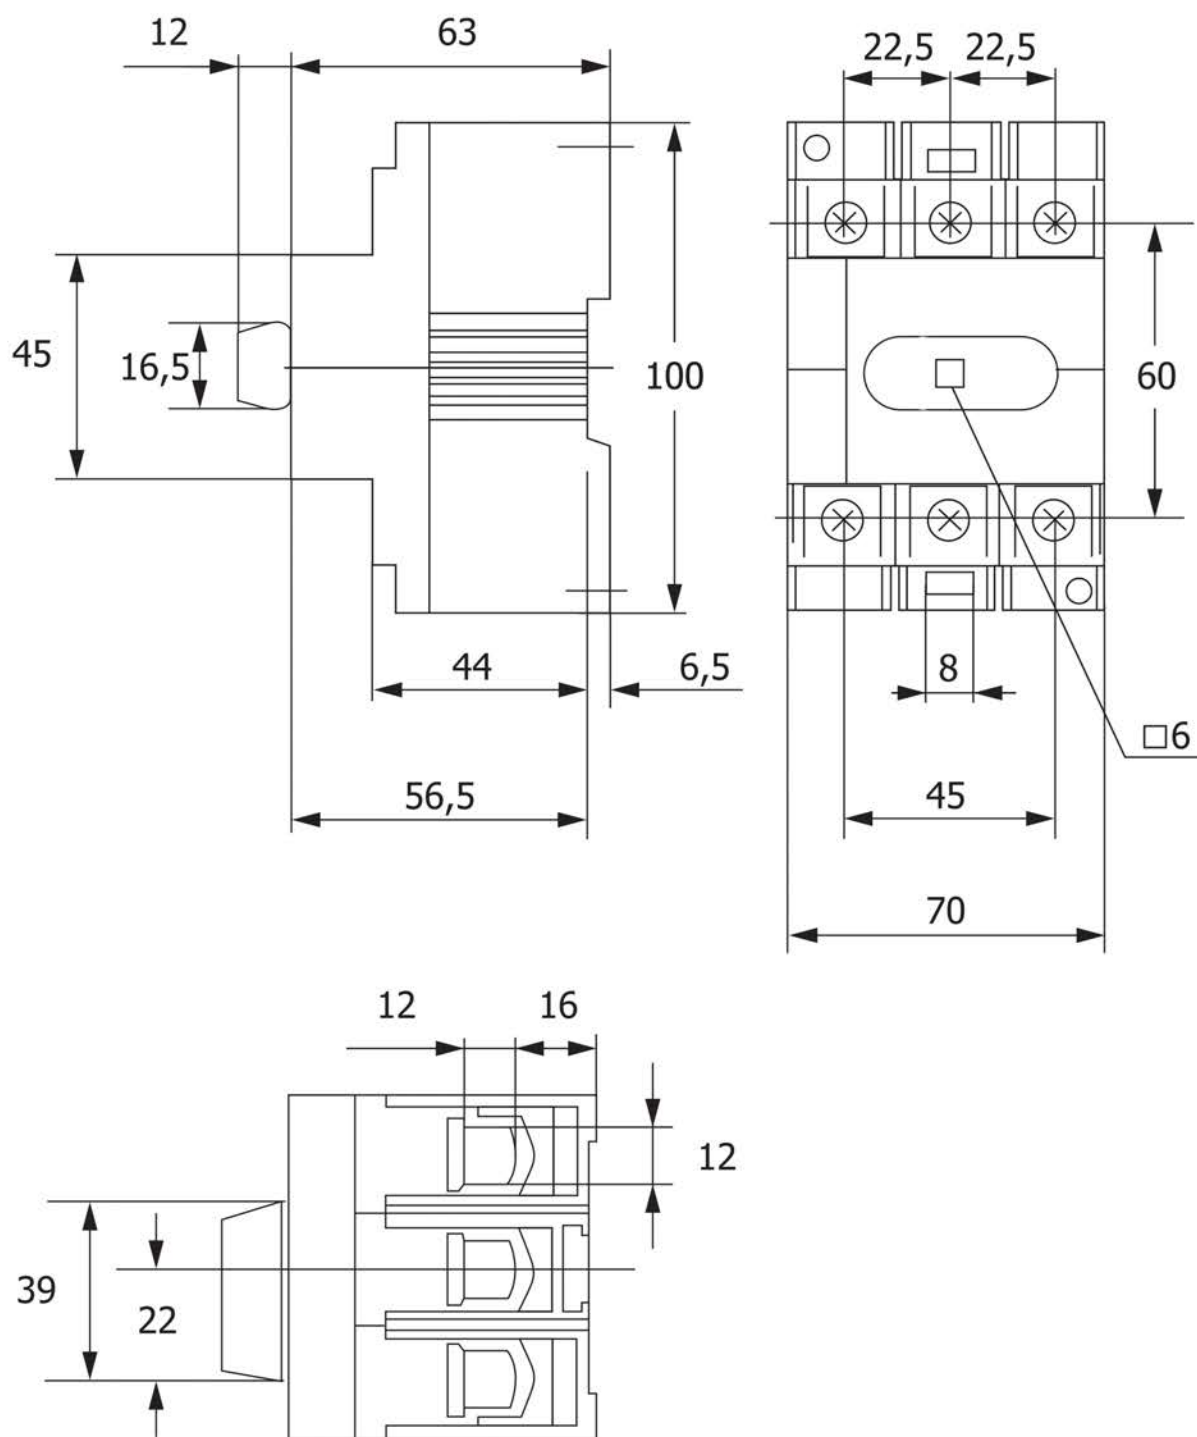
Габаритные и установочные размеры рубильников 40-125А
